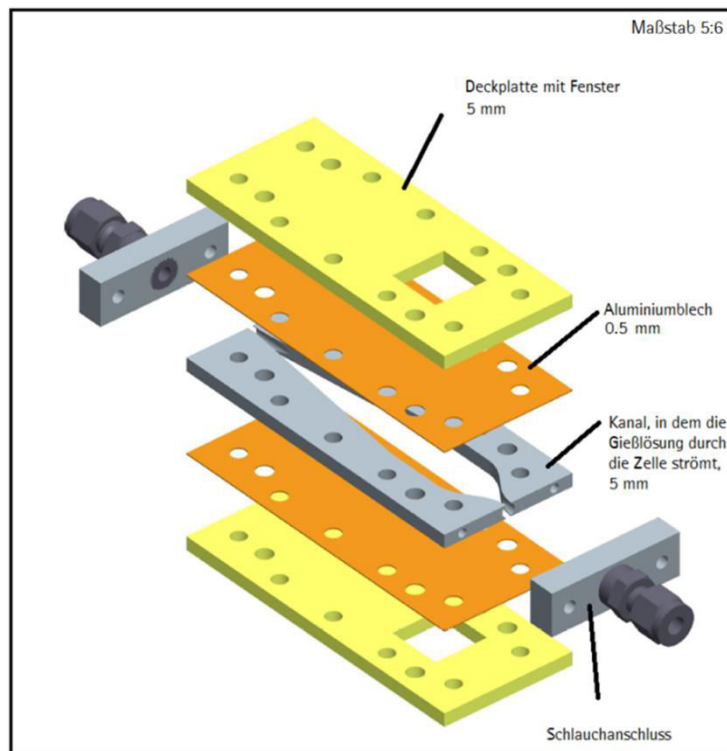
Explosionszeichnung der Messzelle für die SANS-Messung.
